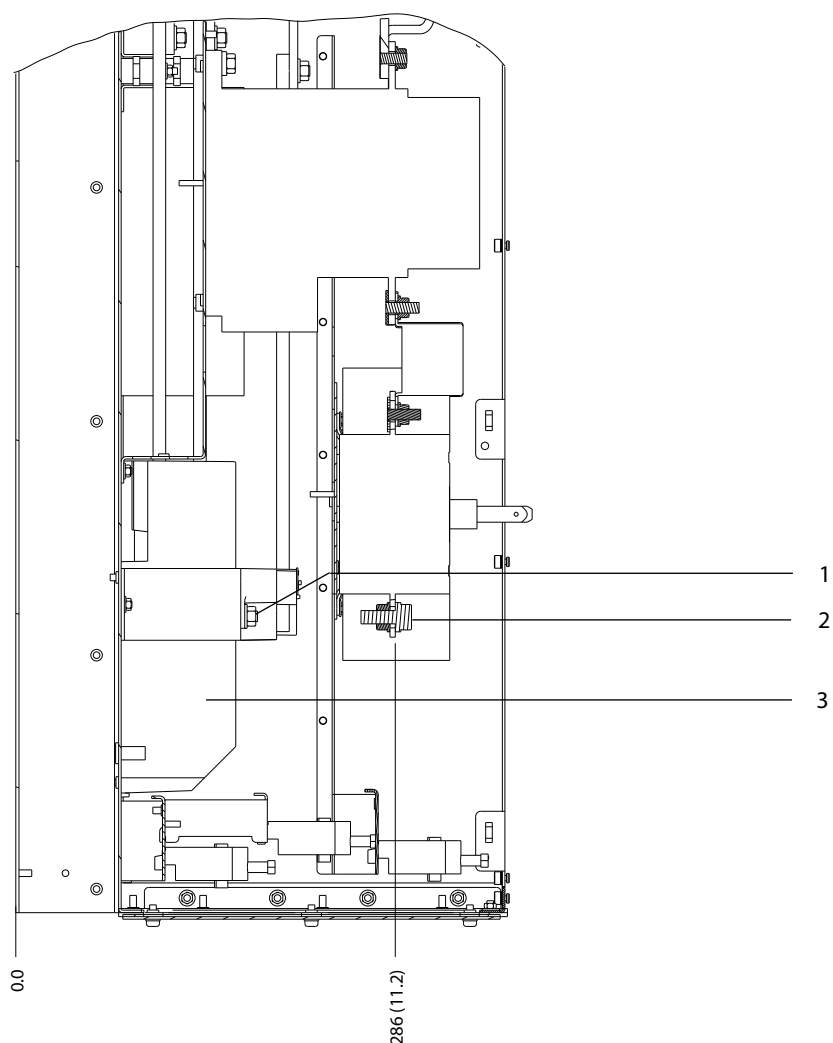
Dimensions des bornes D6h avec option contacteur (vues latérales)
